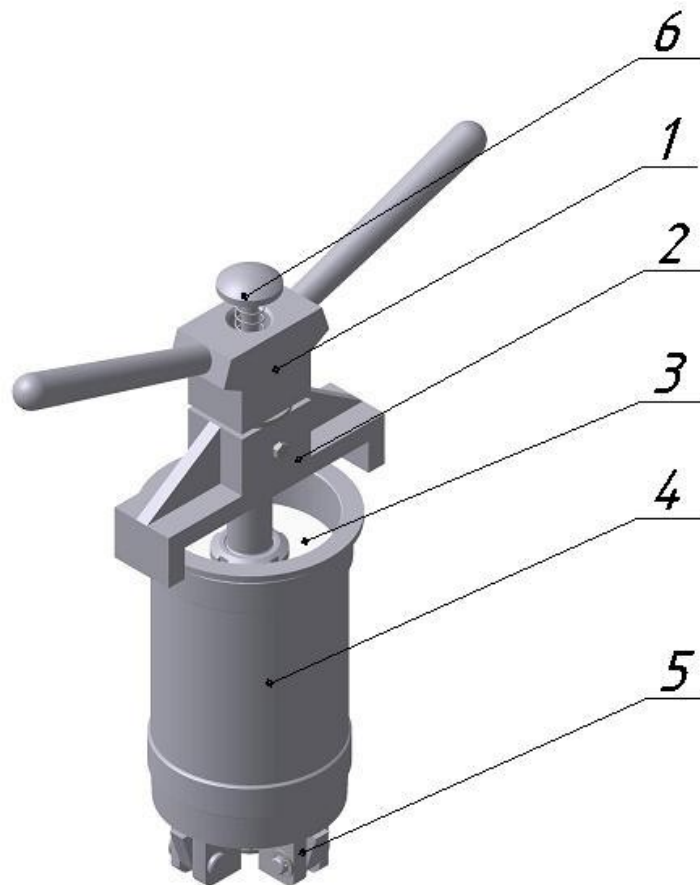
Пристрій для знімання гільз: 1 – гайка; 2 – скоба; 3 – пробка; 4 – гільза; 5 – захоплення; 6 – механізм фіксації.
